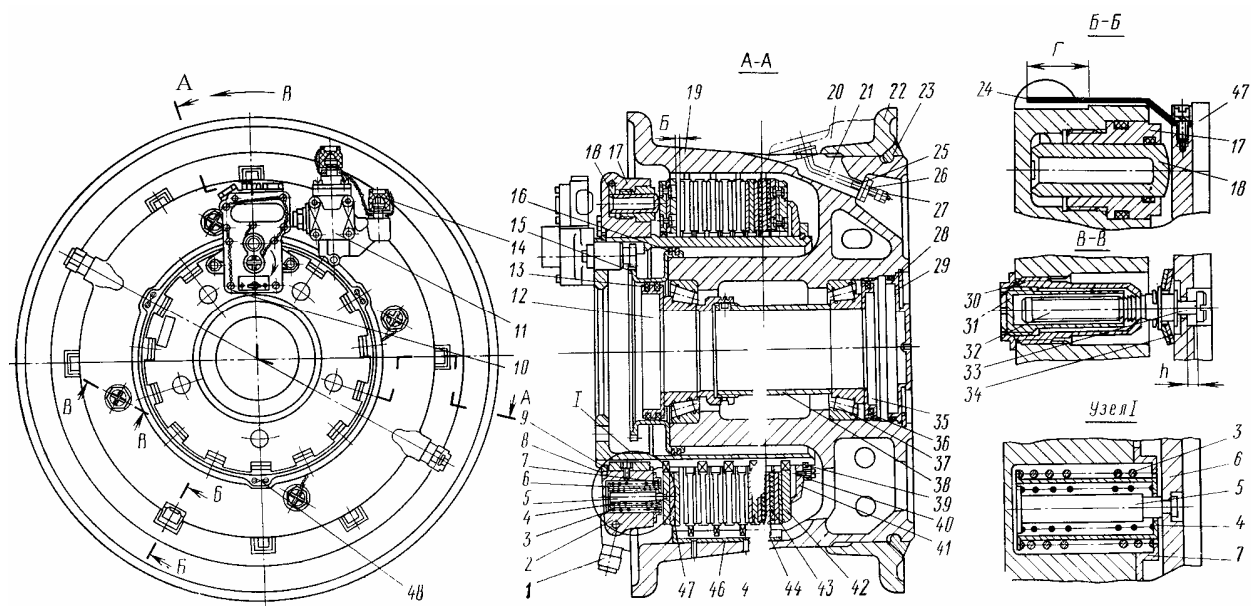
Тормозное колесо КТ-141А000-1 (колесо КТ-141А000-2 — отраженный вид): 1—клапан; 2—блок цилиндров; 3, 4—пружины; 5—стержень; 6—стакан; 7, 29—крышки; 8, 23, 28, 35—стопорные кольца; 9—стопорное полукольцо; 10—антиюзный автомат; 11—челночный клапан; 12, 35—обоймы; 13, 36—манжеты; 14—заглушка; 15—шестерня; 16, 40—кольца; 17—гильза; 18—поршень; 19—барабан; 20—шина; 21—вентиль; 22—реборда; 23—стопорное кольцо; 24—указатель износа; 25—шайба; 26—гайка; 27—колпачок; 30—цанга; 31—режим; 32—упор; 33—специальный винт; 34—тарельчатые пружины; 37—роликовый подшипник; 38—распорная втулка; 41—фланец; 42—опорный диск; 43—корпус пистона; 44—металлокерамический диск; 45—промежуточный диск; 46—направляющая; 47—нажимной диск; 48—винт; Б—суммарный зазор после растормаживания; В—направление вращения колеса; Г—размер, указывающий на максимальное обжатие пружины узла растормаживания; h—зазор между тарельчатой пружиной и нажимным диском
